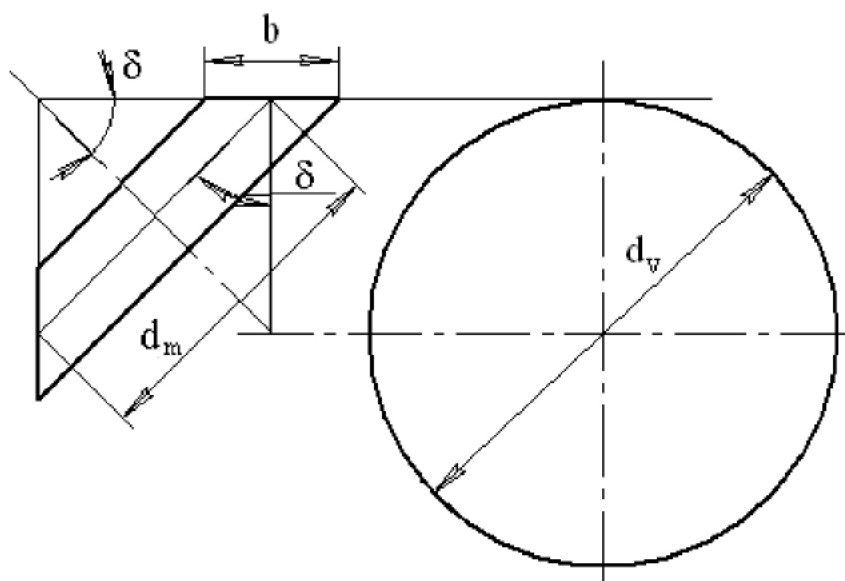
Схема определения размеров цилиндрического колеса, эквивалентного коническому
